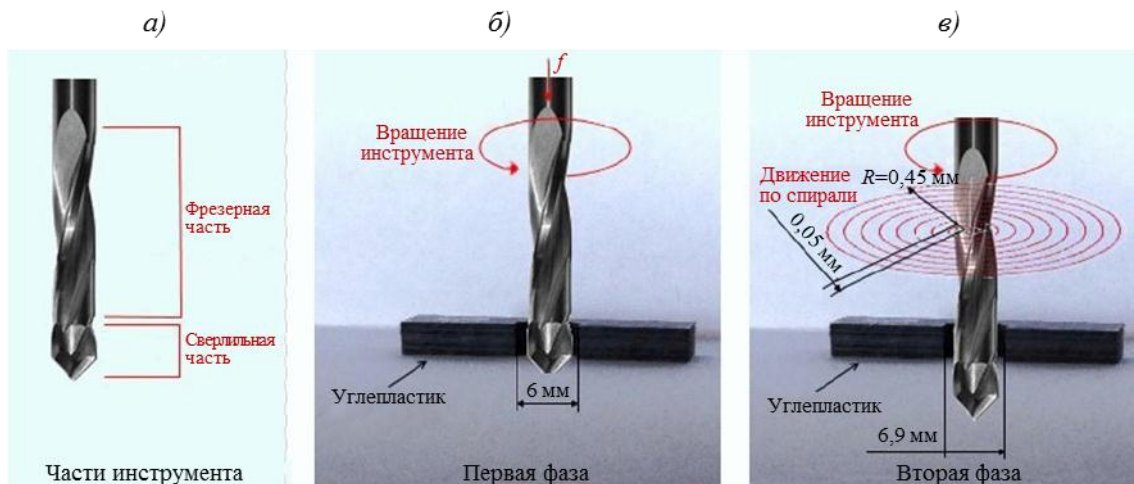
Сочетание сверления и фрезерования при выполнении отверстий: а – конструкция инструмента; б – сверление; в – периферийное фрезерование
